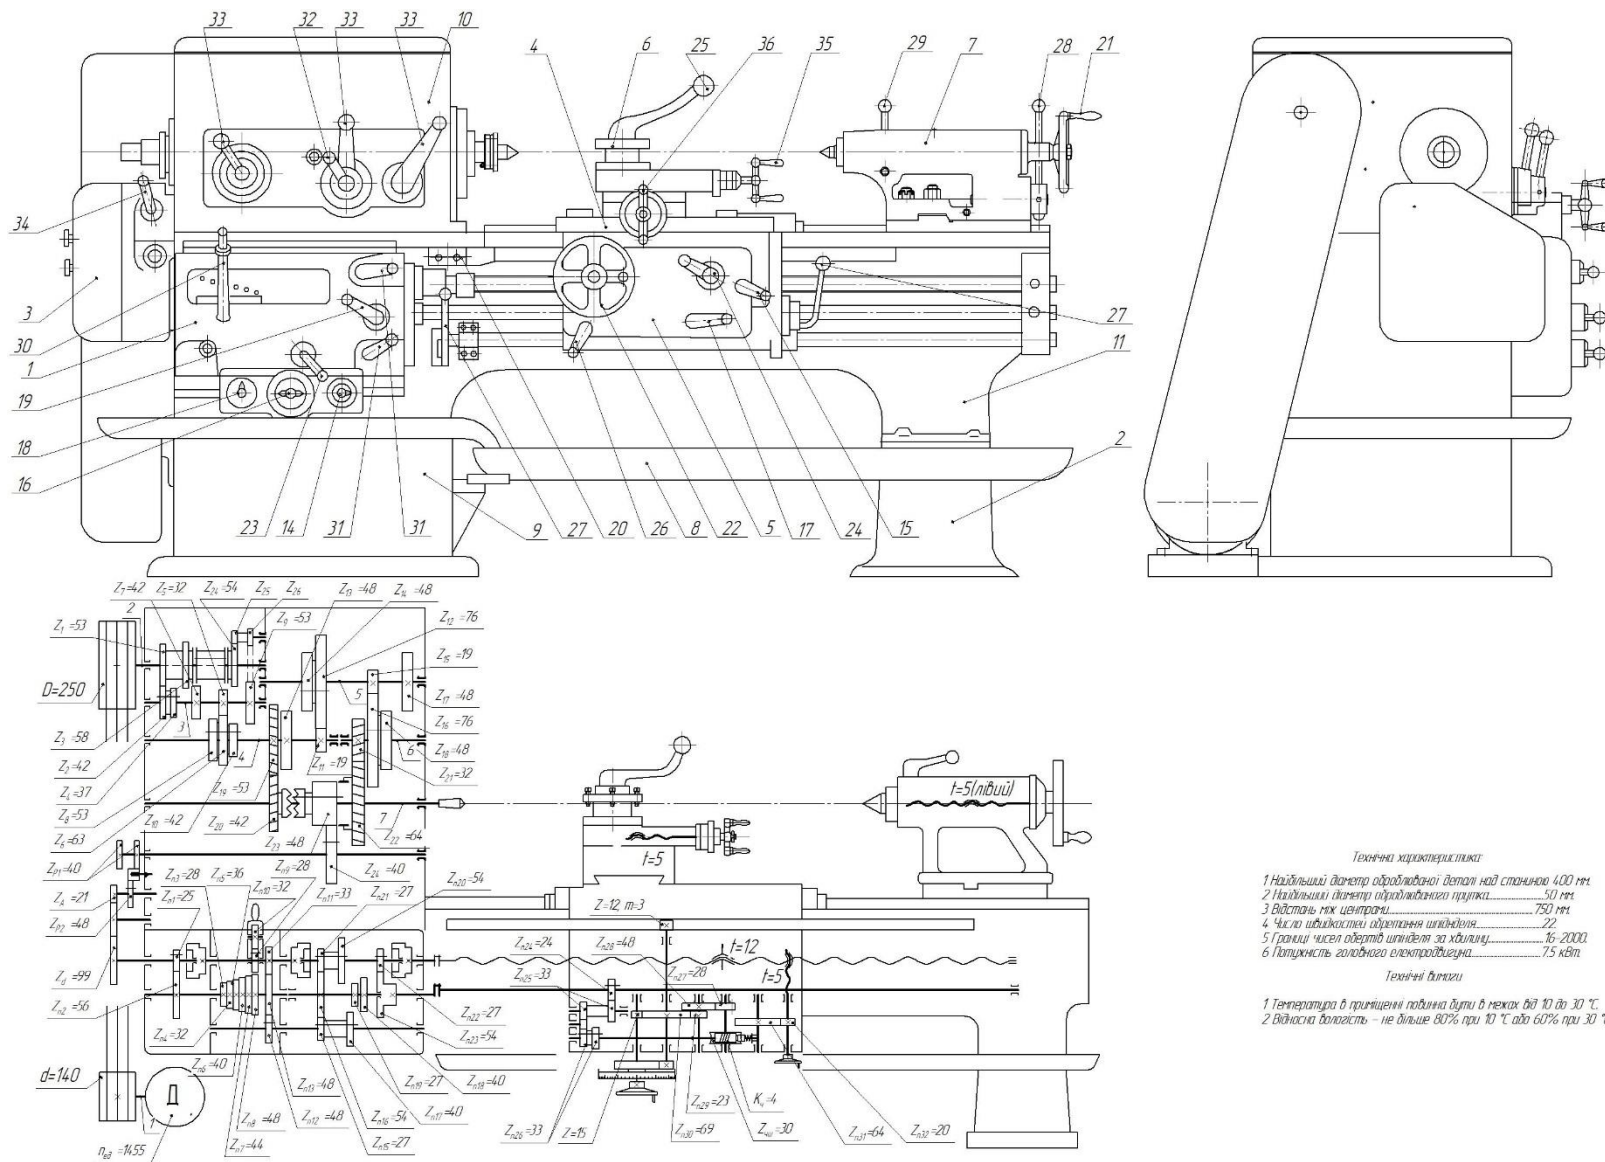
Загальний вигляд і кінематична схема верстата 1А62
